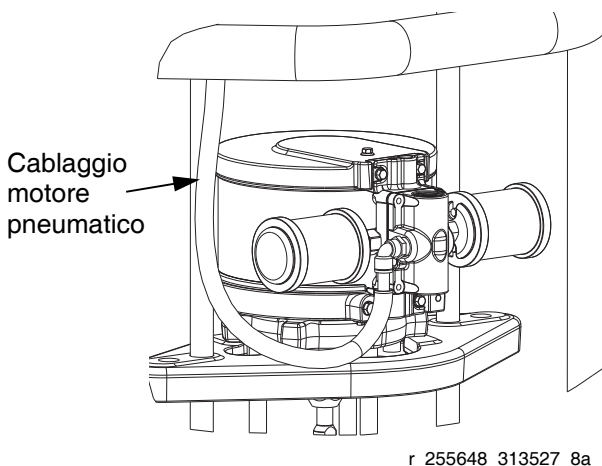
Cablaggio motore pneumatico NXT 200-1800
